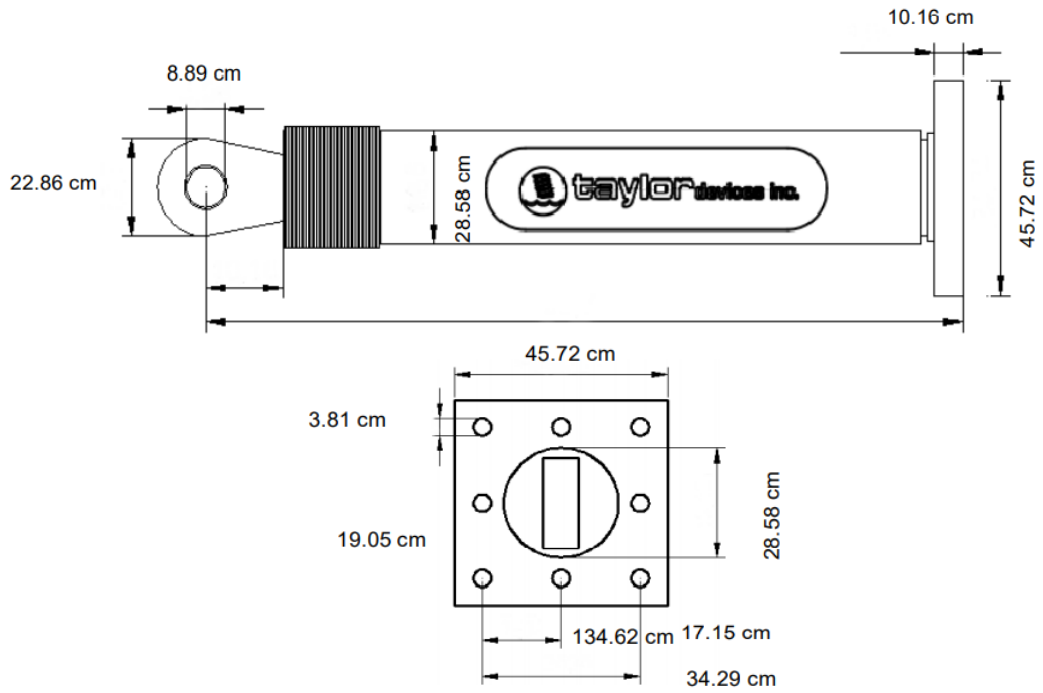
Dimensiones de disipador y placa base de 440 Kip.
